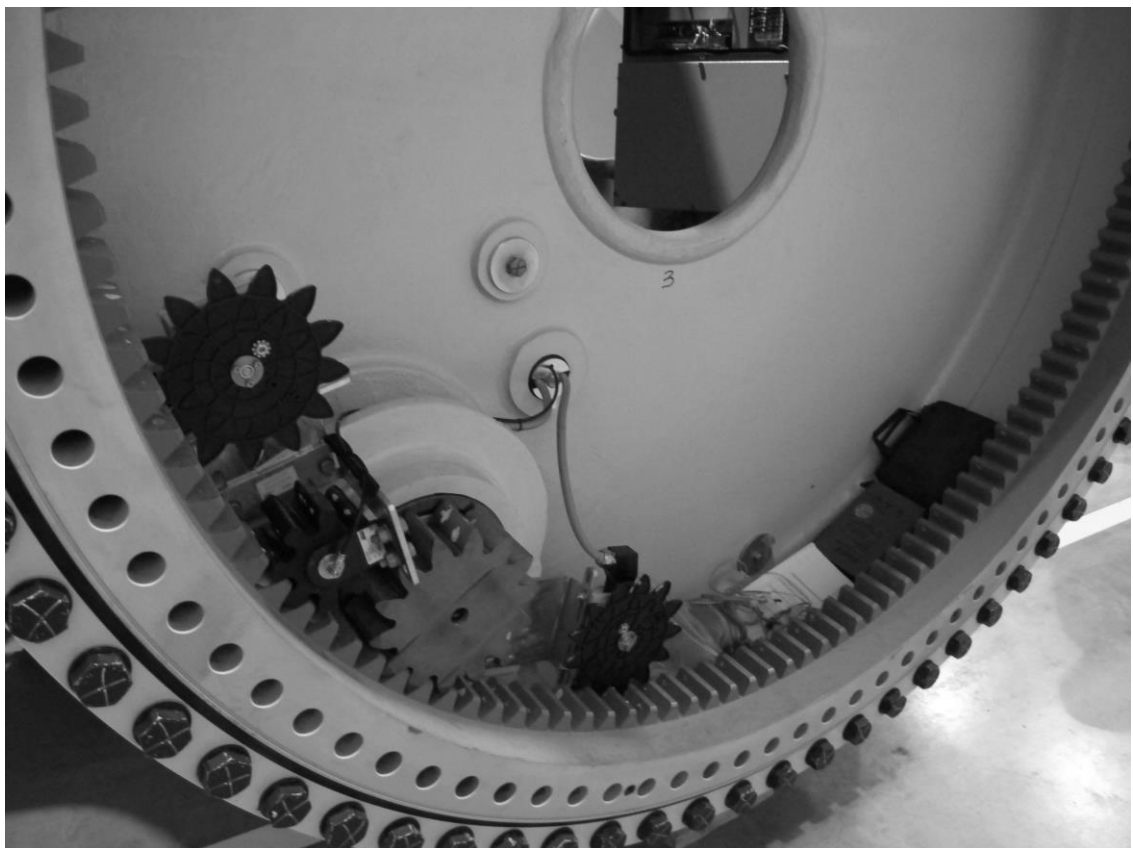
Вид зубчатой передачи и датчиков положения привода поворота лопасти ветроустановки Fuhrlander
